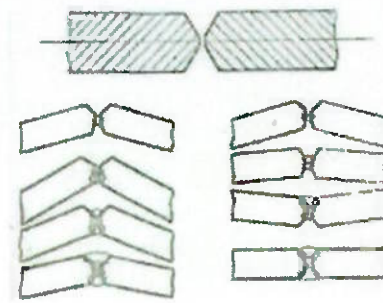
Sequência de soldagem do chanfro simétrico [15].
